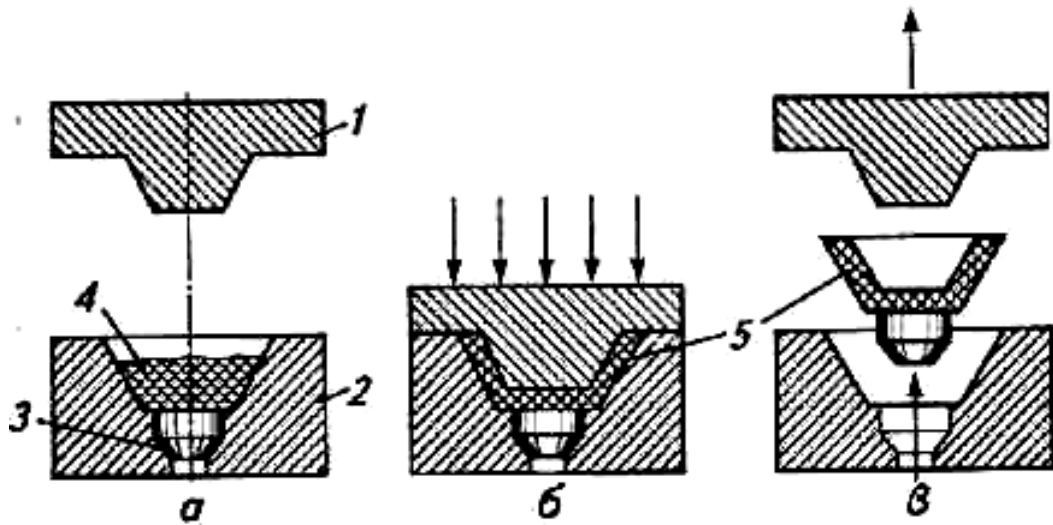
Схема изготовления деталей из пластмасс методом горячего прессования: а - исходное положение; б - прессование; в - удаление из пресс-формы; 1 - пуансон; 2 - матрица; 3 - толкатель; 4 - пресс-материал; 5 - изделие
